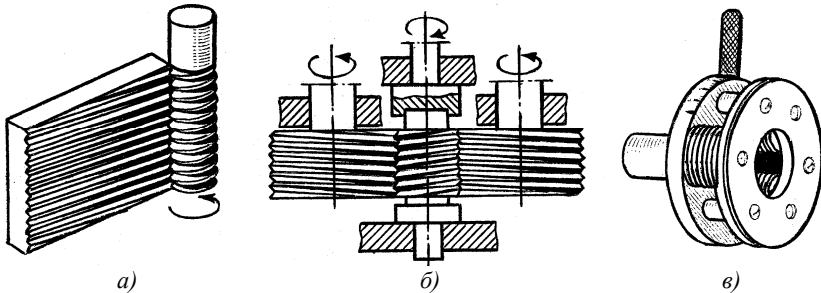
Схема виготовлення різьби накатуванням:
